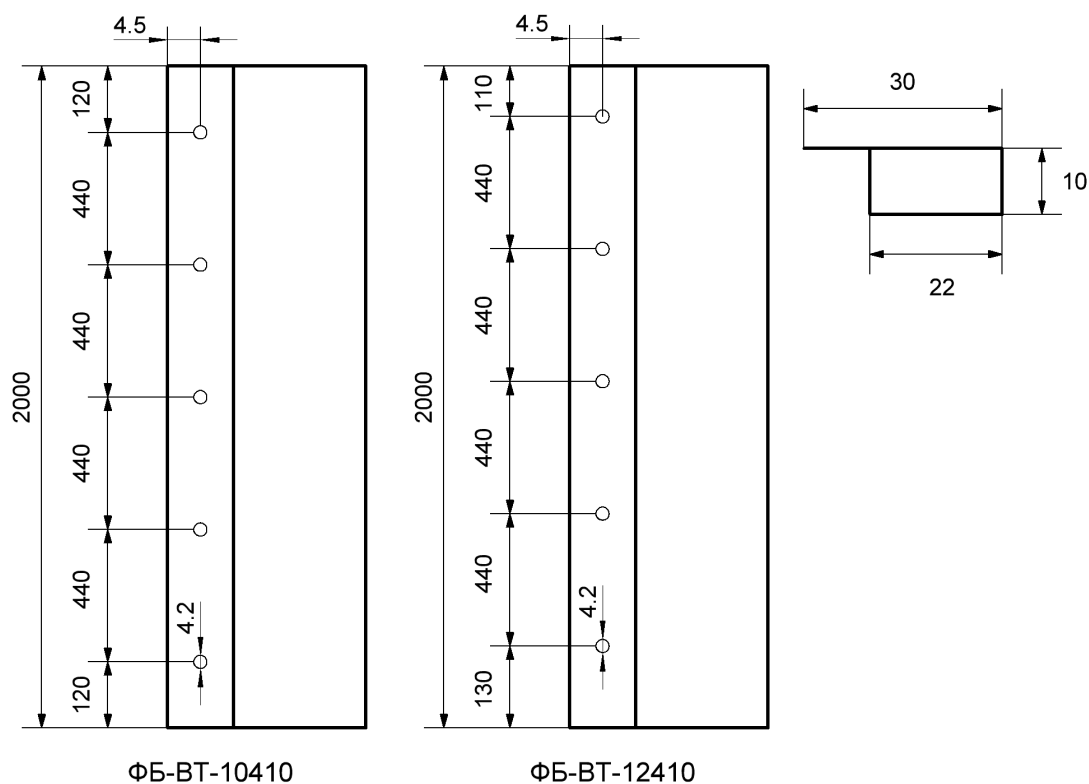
Габаритные размеры фотобарьера (в мм)
